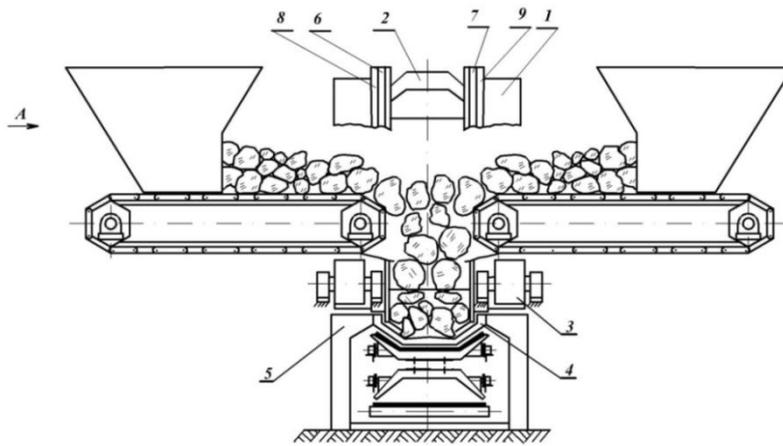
Общий вид лопастного питателя с двухсторонней загрузкой конвейера
